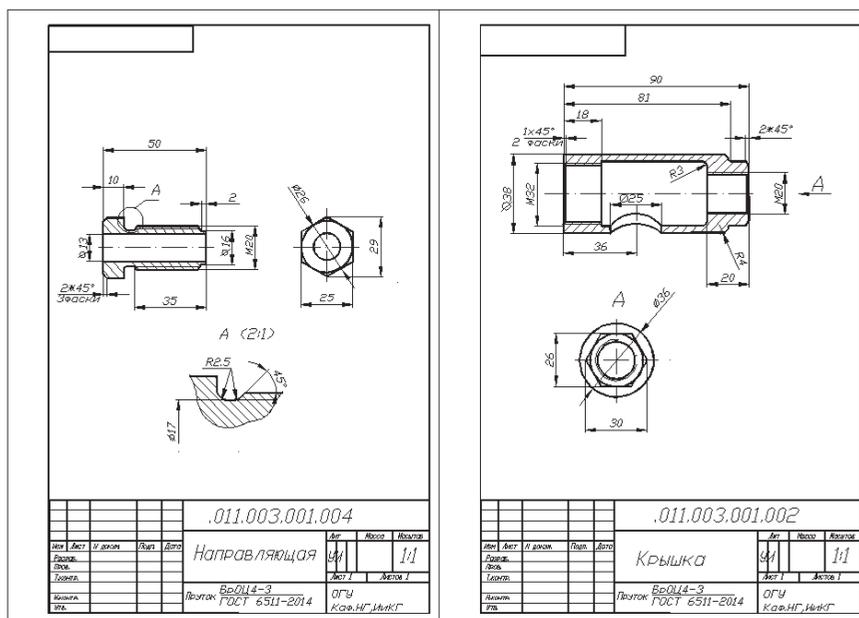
Примеры 2D-моделей (чертежей) деталей сборки изделия «Клапан предохранительный»
